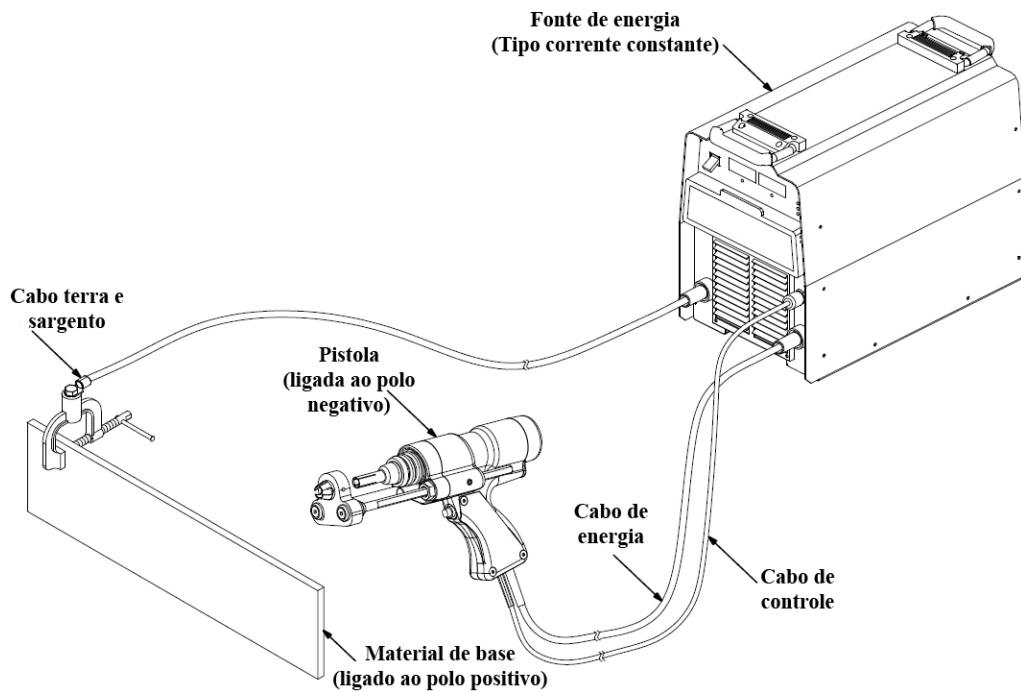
Equipamento de soldagem por eletro fusão (Manual Miller, 2012).
